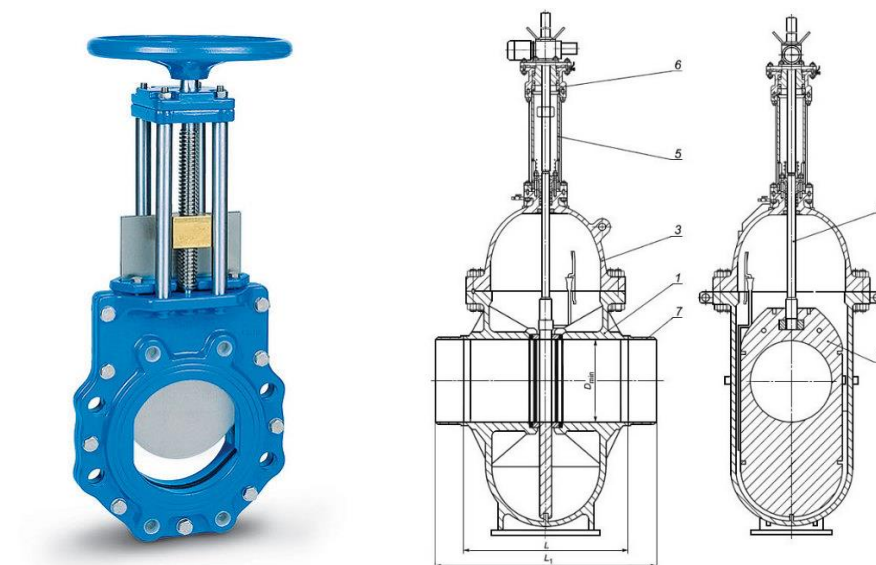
Внешний вид и чертеж задвижки и ее основные части:
